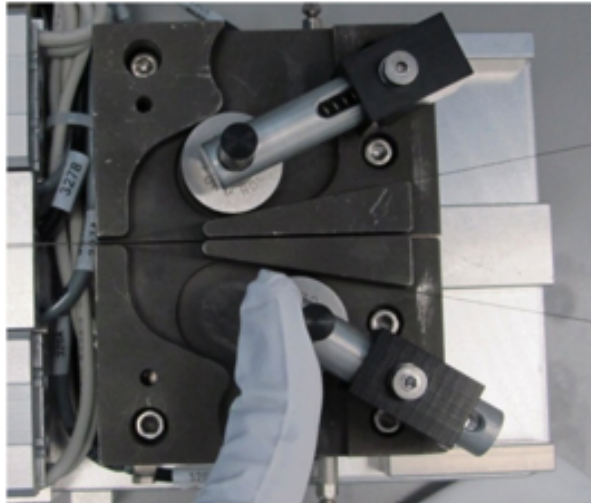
Libere los Cables de tiraje de las Abrazaderas
